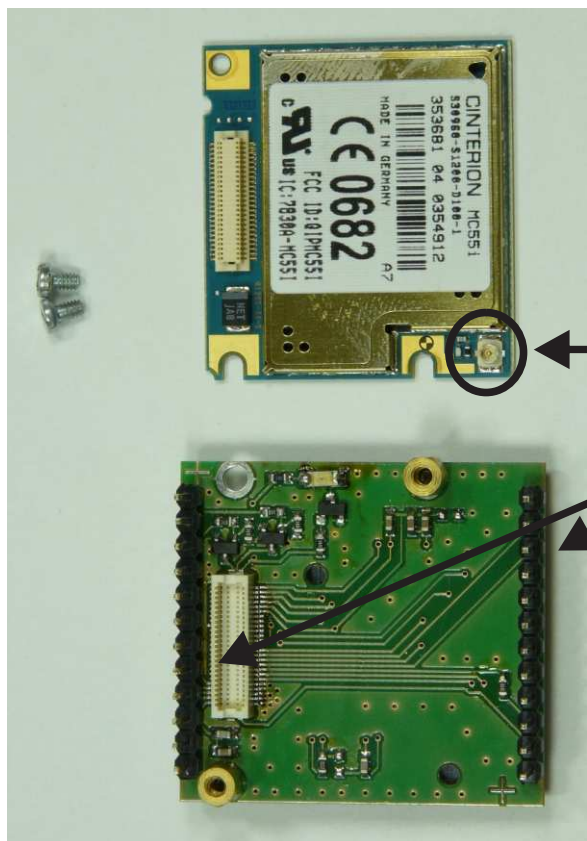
PCB – matična ploča sa SMT i Trough hole komponentama spremna za montažu.
